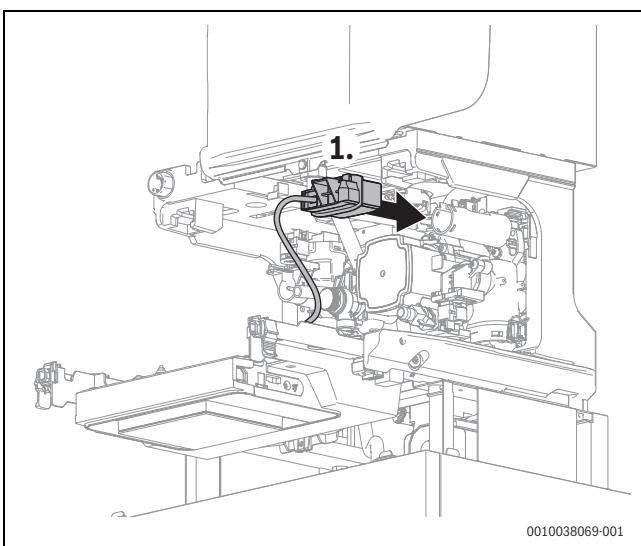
Key-Halter auf die Rückseite des Geräts führen
